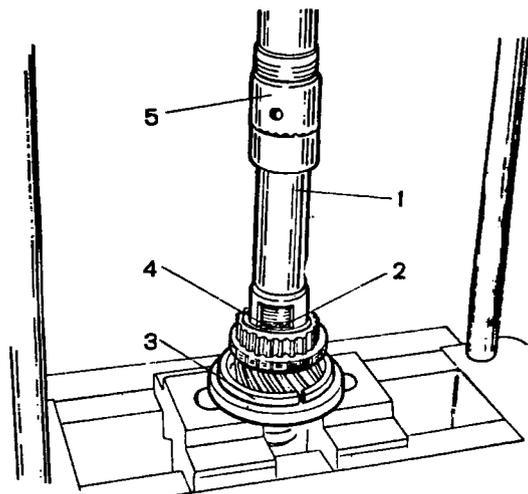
Установка на вторичном валу стопорного кольца: 1 - оправка 41.7816.4069; 2 - стопорное кольцо; 3 - опорное полукольцо; 4 - пружинная шайба; 5 - шток пресса
